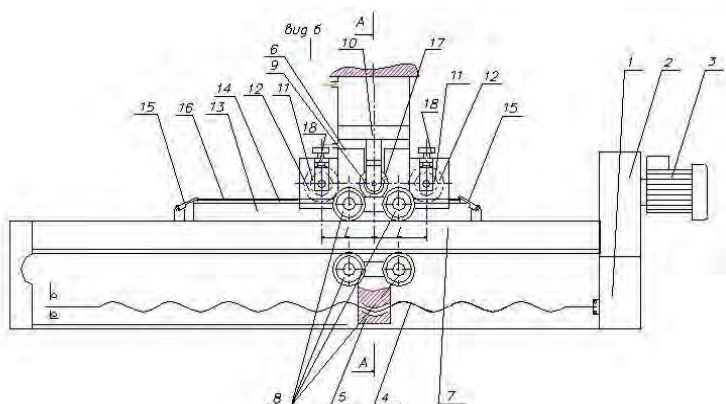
Схема стана локальной формовки с двумя эластичными валами и подвижной траверсой [8]
